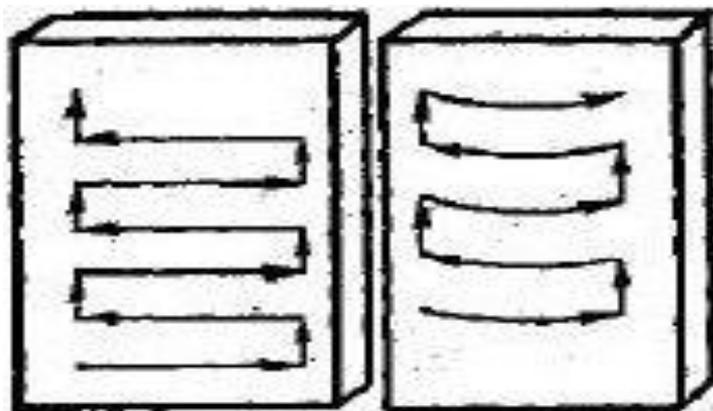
Схема движения электрода при выполнении широких валиков при сварке стыковых соединений в вертикальном положении
